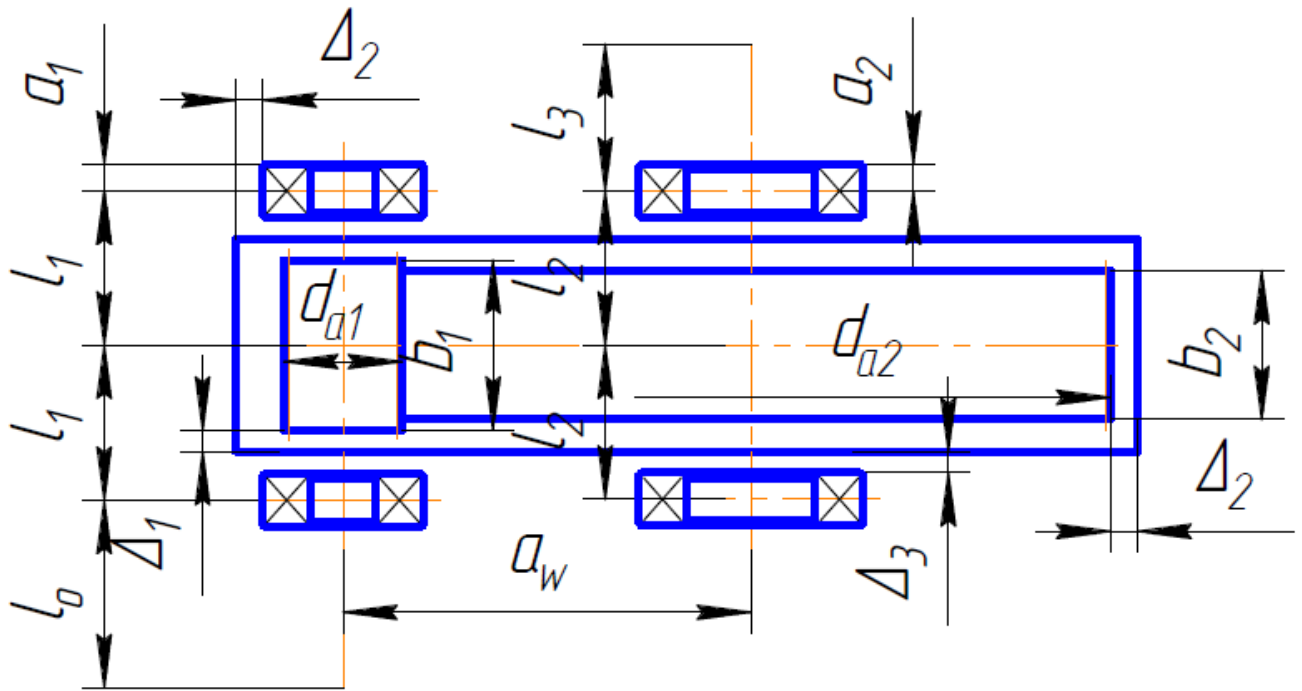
Приклад ескізної компоновки циліндричного редуктора
